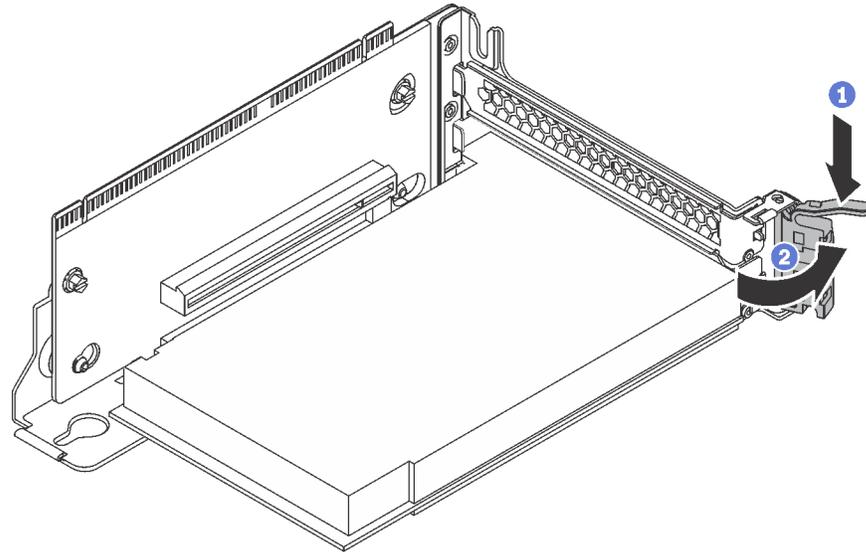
Apertura del mecanismo de cierre de sujeción del adaptador PCIe
